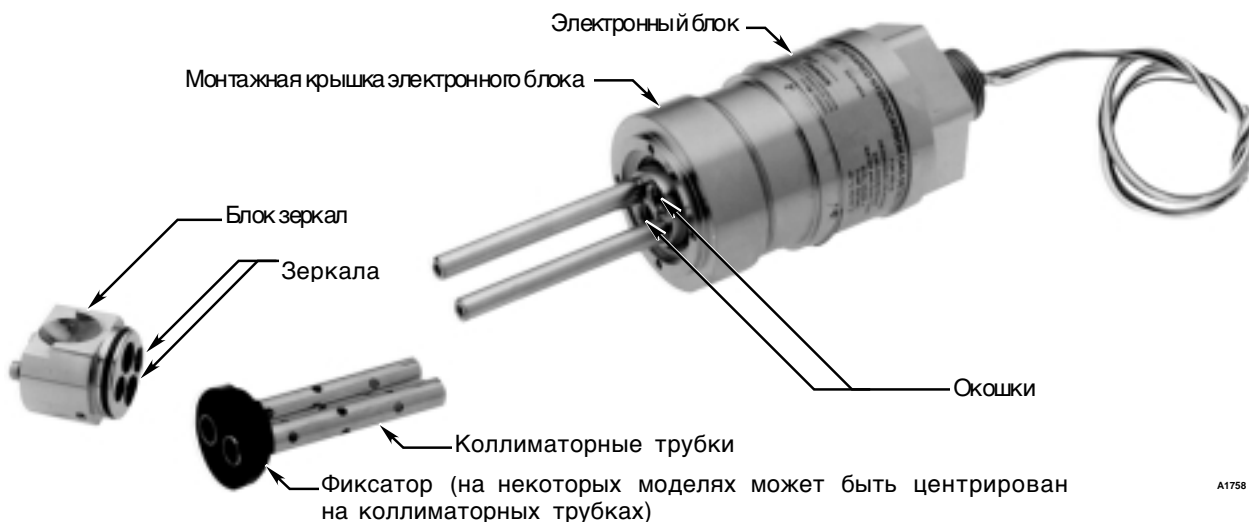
Демонтаж для проведения чистки детектора ПойнтВотч в корпусе из нержавеющей стали.
